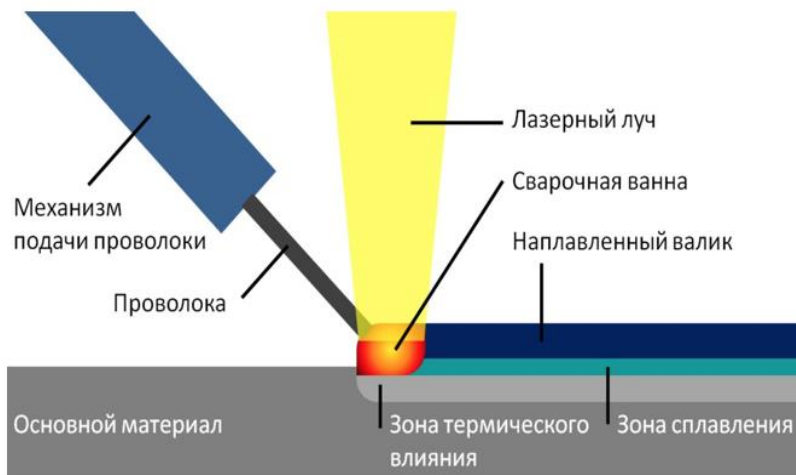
Процесс лазерной наплавки и модифицирования поверхностного слоя материала обрабатываемой детали с принудительной подачей легирующей проволоки в зону сварочной ванны [206]
